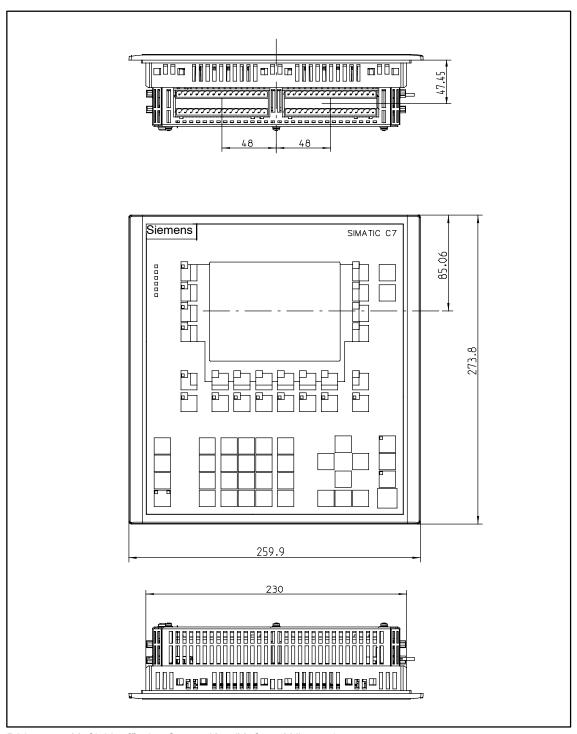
Maßbilder für das C7-635 Key (Maße in Millimeter)
